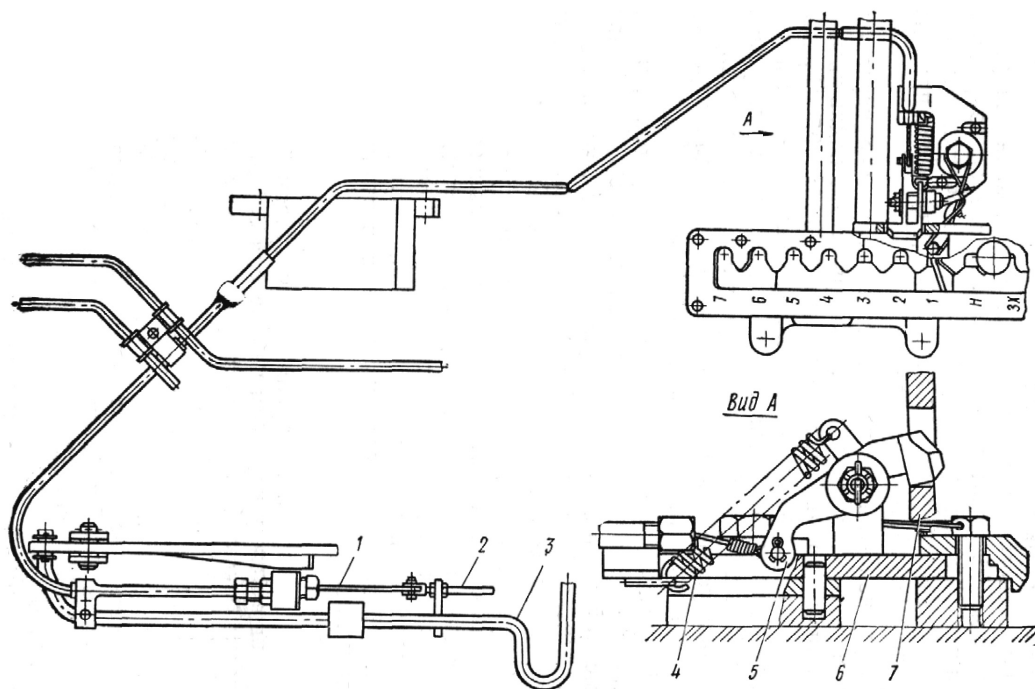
Блокировка избирателя передач от защелки педали остановочного тормоза: 1 – трос; 2 – вилка регулировочная; 3 – тяга защелки остановочного тормоза; 4 – пружина возвратная; 5 – рычаг; 6 – плита; 7 – рычаг избирателя передач
